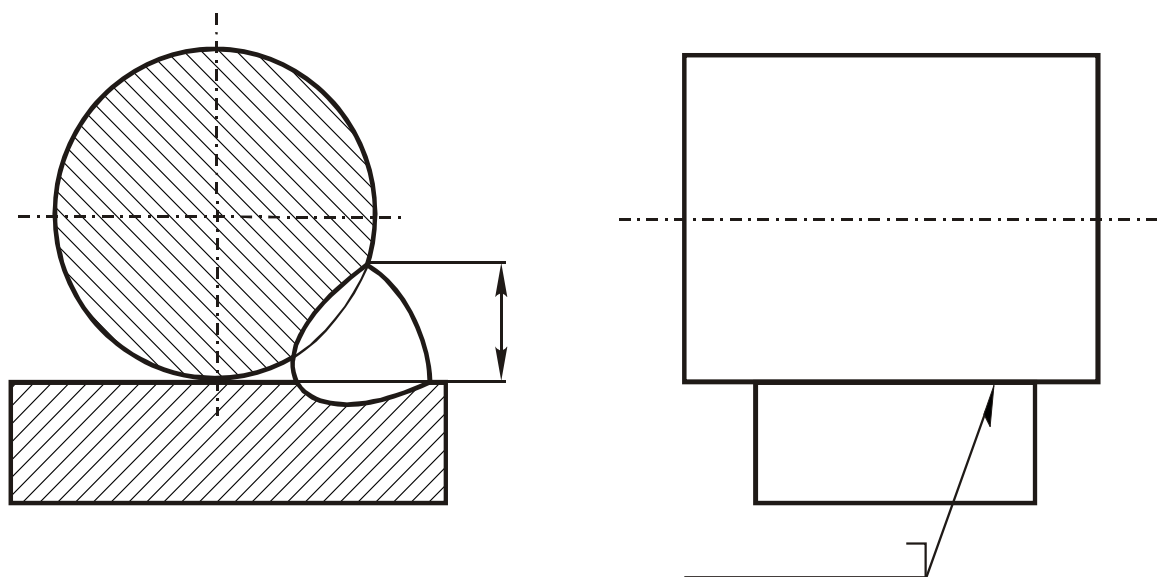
Обозначение нестандартного сварного шва
